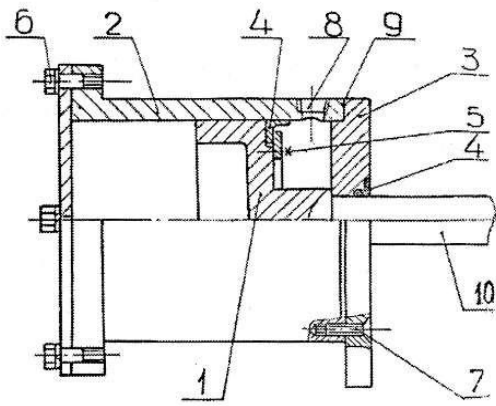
Пневматичний циліндр перестановки барабанів
